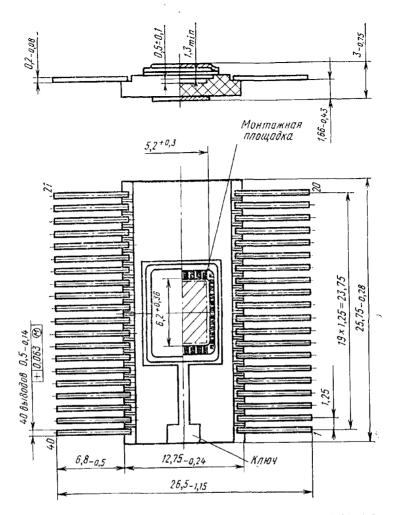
Конструкция металлокерамического корпуса 4122.40-2
